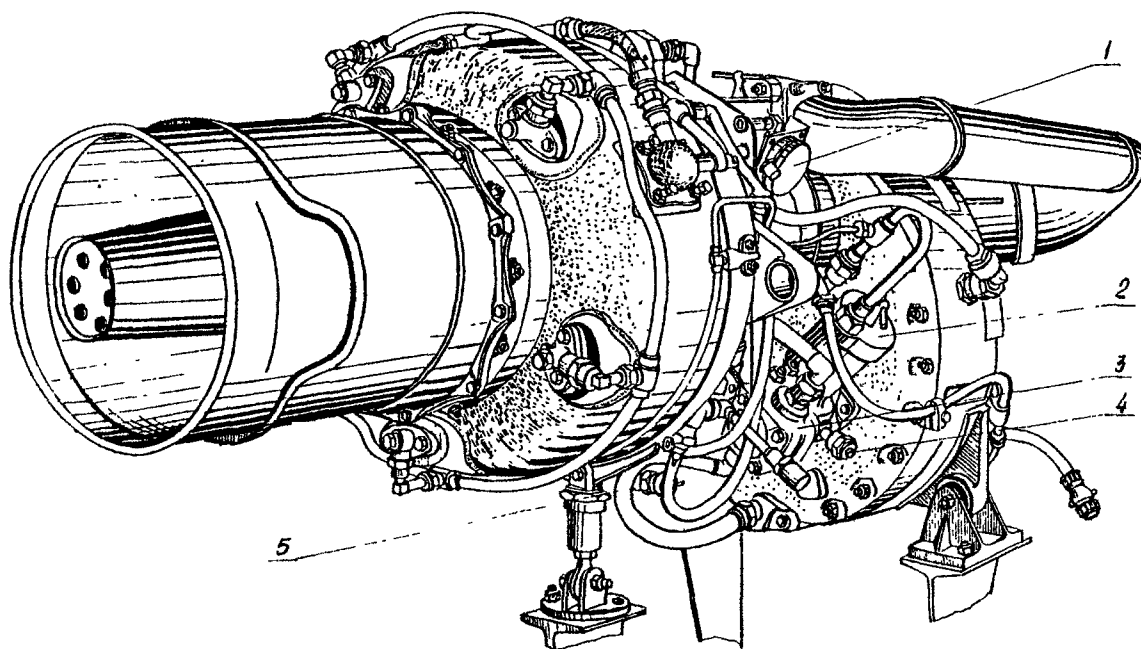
Внешний вид бортовой установки ТГ-16М (вид сзади - справа).
